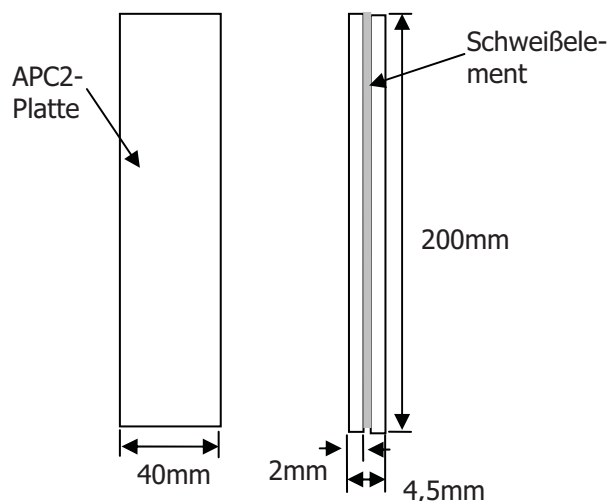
APC2-APC2 Schweißprobenkonfiguration A
